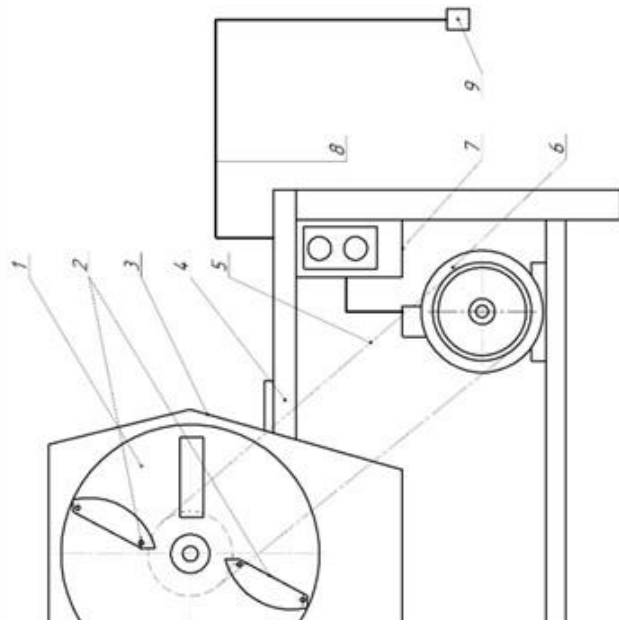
Конструкційна схема каліно-дискового подрібнювального кормів: 1 – диск; 2 – корпус; 4 – рама; 5 – пасова передача; 6 – електропривод; 7 – керування; 8 – мережевий
